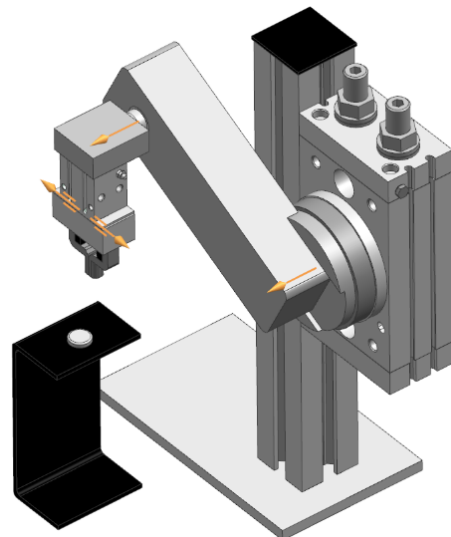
Juntas de la etapa "Inserción del rodamiento".
